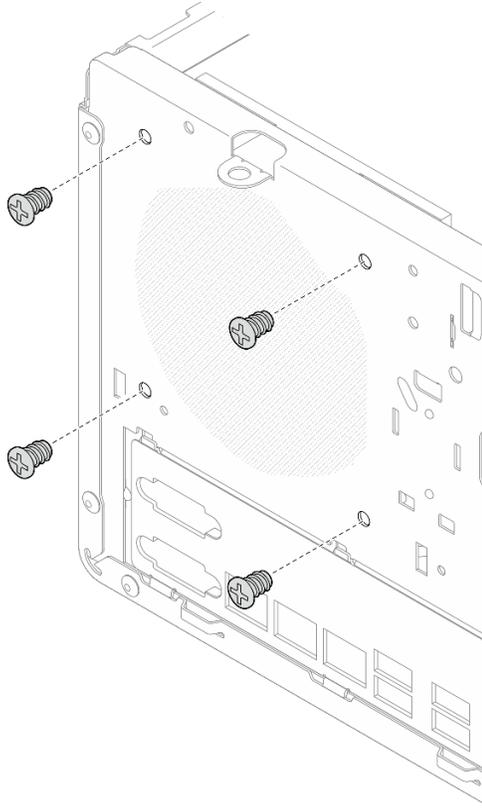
Installation du ventilateur du dissipateur thermique sur l'arrière du châssis
